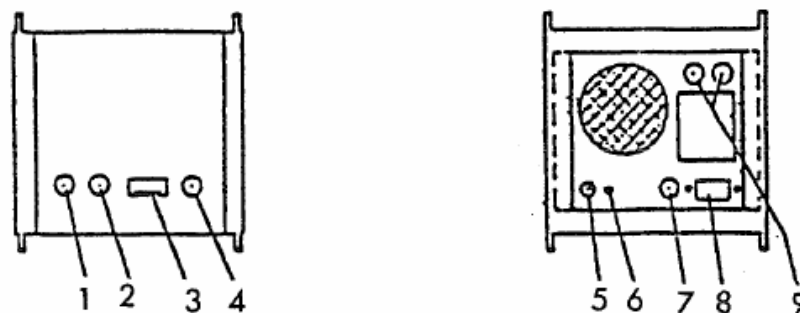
Ультразвуковой сварочный аппарат.
